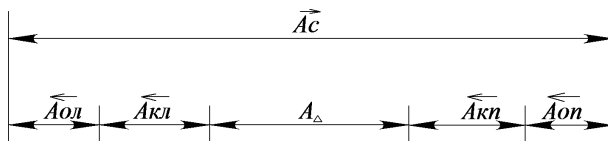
Размерная цепь по оси колесной пары в процессе сборки
